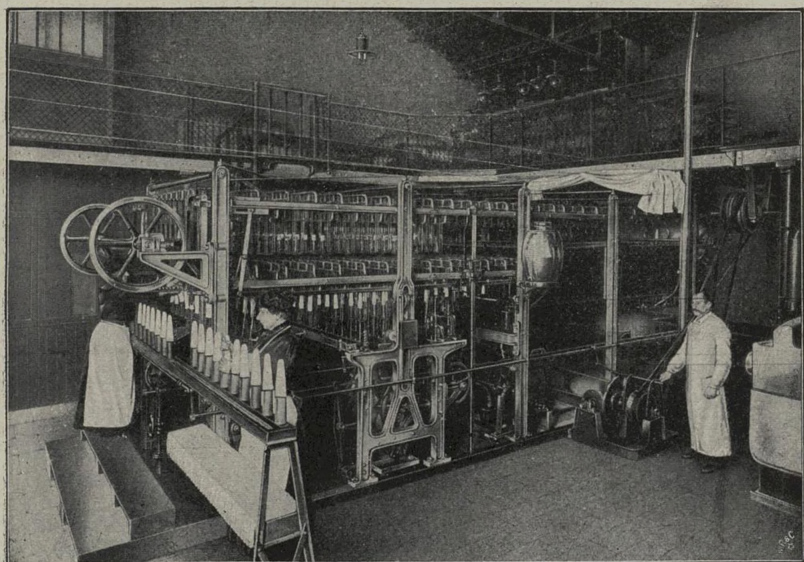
Accrochage des manchons et vue d'ensemble (Machine Muller et Bonnet).
